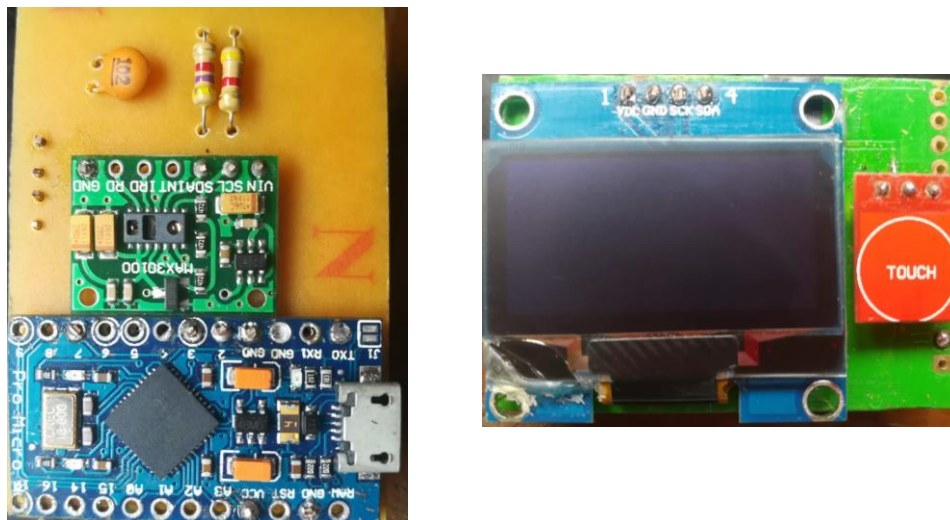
Diseño PCB del sensor MAX30100, pantalla y microcontrolador.
